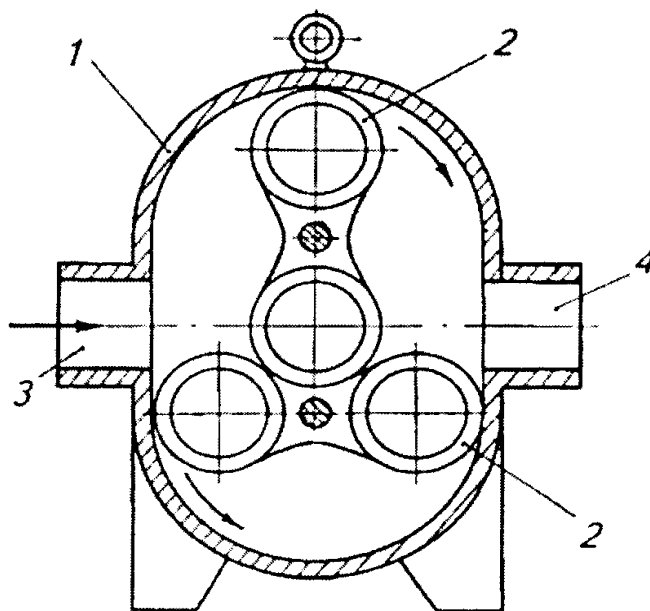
Схема двухроторной машины: 1 – корпус; 2 – ротор; 3 – всасывающий патрубок; 4 – нагнетательный патрубок
